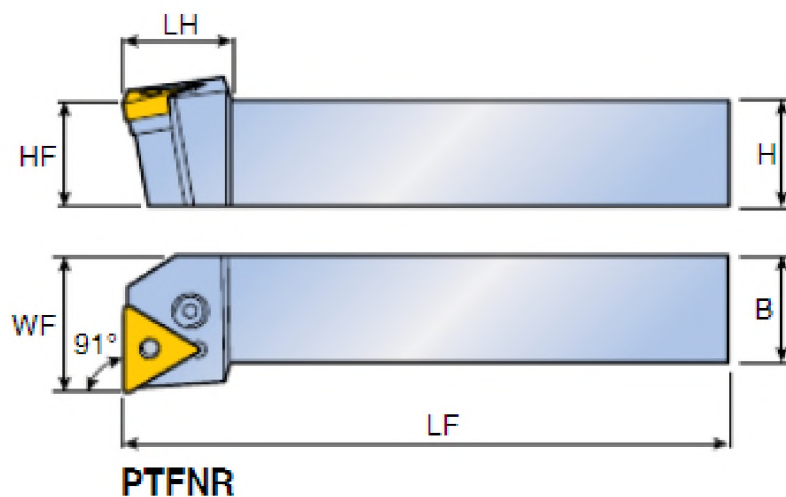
Державка PTFNR 2525 M16 [1, с. A77]:
